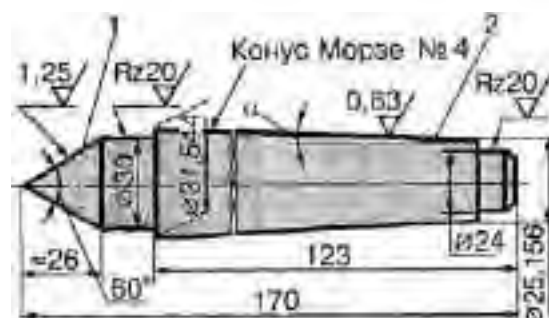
ЖОРСТКИЙ ЦЕНТР
